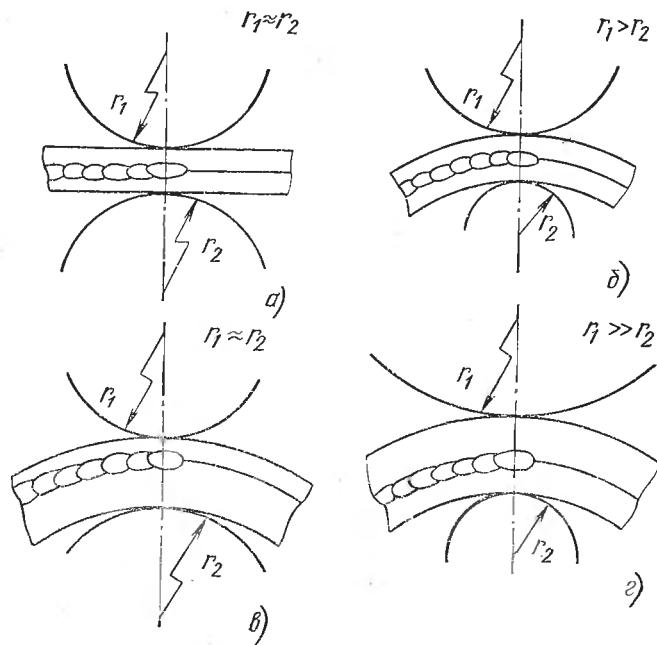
Выбор диаметра роликов при шовной сварке
